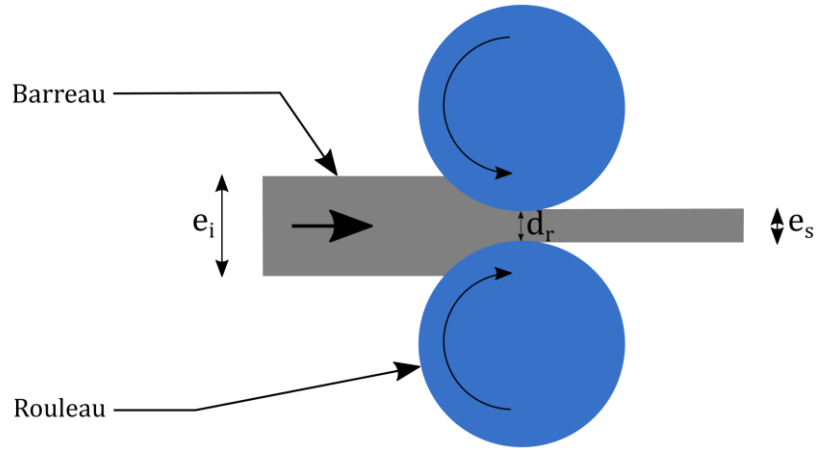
Schéma illustrant le principe du fonctionnement d'un laminoir plan.
